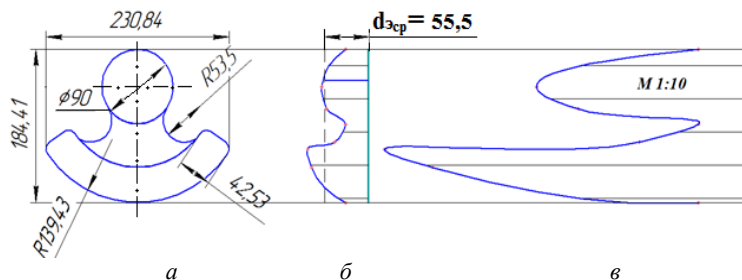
Поковка «Суппорт» (а), эпюра сечений (б) и эпюра диаметров (в)
